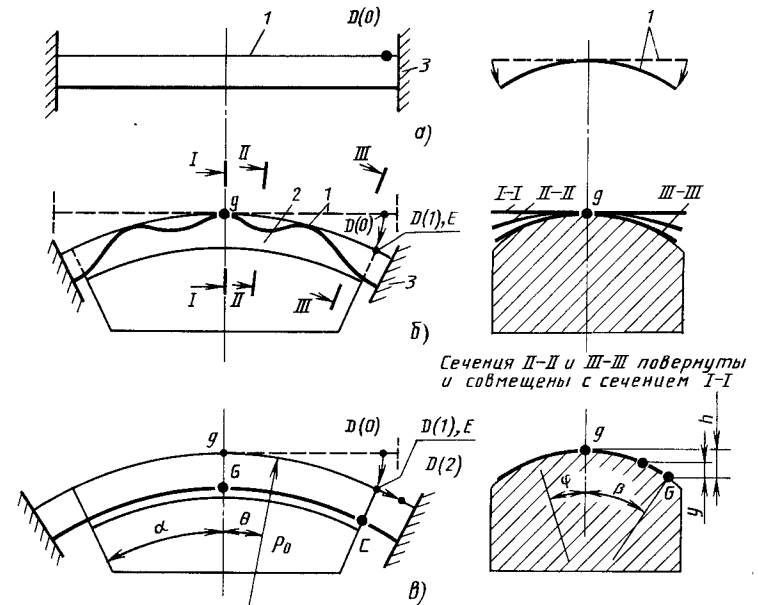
Последовательность обтяжки инструмента с двояковыпуклой поверхностью: а — гибка листа в цилиндрическую оболочку; б — наматывание на пуансон (сечения II—II и III—III повернуты и совмещены с сечением I—I); в — обтяжка; 1 — заготовка; 2 — пуансон; 3 — захват
